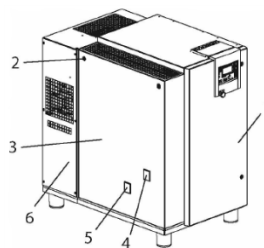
Корпус компрессора: 1 – дверь распределительного шкафа; 2 – задвижка; 3 – часть обшивки (вставная модель); 4 – смотровой глазок указателя уровня масла; 5 – смотровой глазок натяжения ремней; шкаф с холодоосушителем
